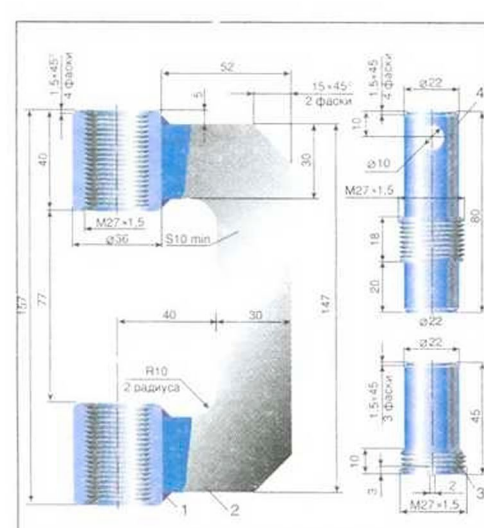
Приспособление для выпрессовки и запрессовки подшипников карданного вала автомобилей ВАЗ-2101...-2107. 1 - резьбовая втулка, 2 - струбцина, 3 - винт-упор, 4 - винт с отверстием под вороток
